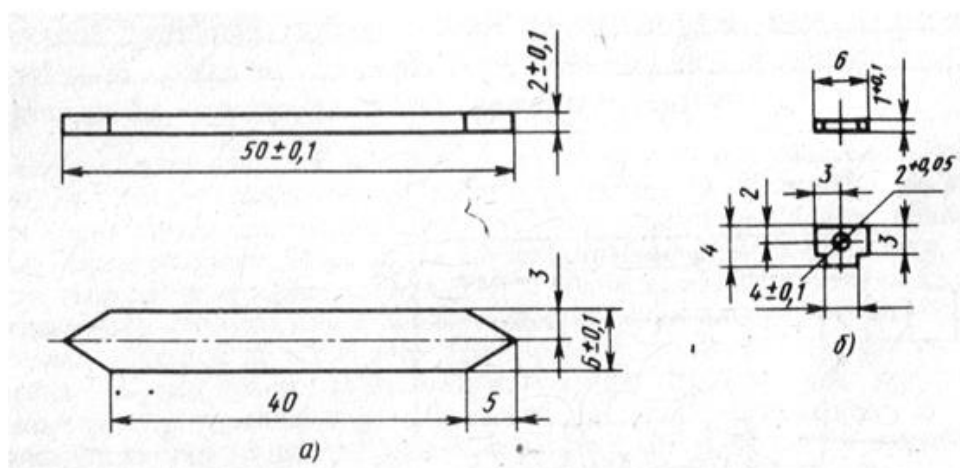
Робочі креслення дослідних зразків. а – нерухомий; б – рухомий;
